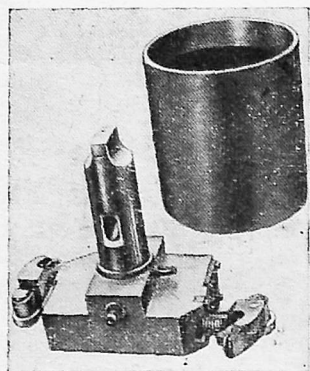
Приспособление для обкатки роликами внутренних поверхностей.
